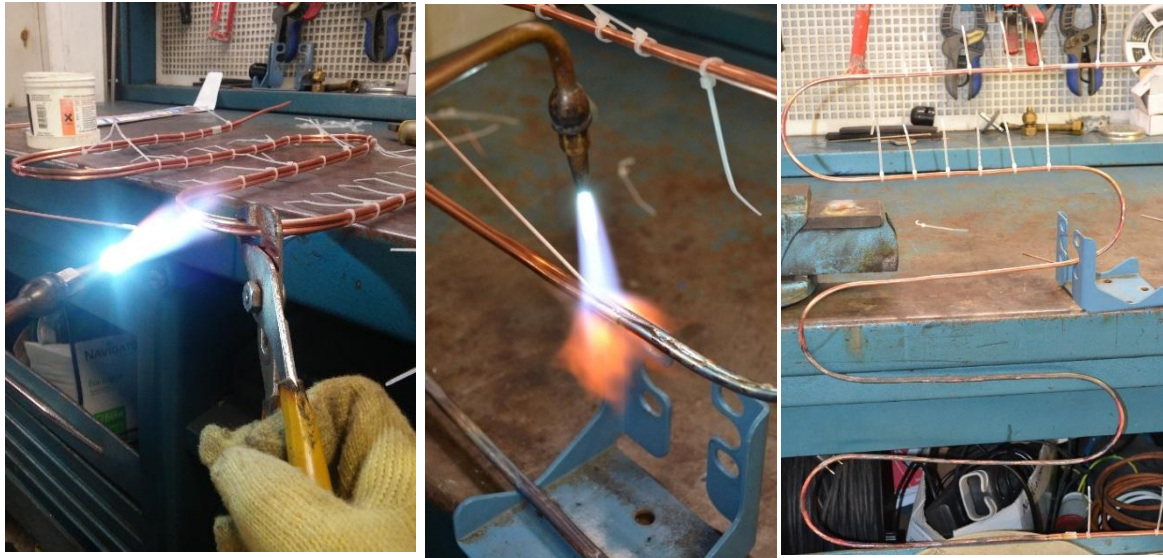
Proceso de soldadura del condensador equivalente.
